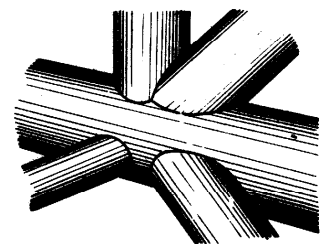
Соединение труб, подготовленное к сварке
